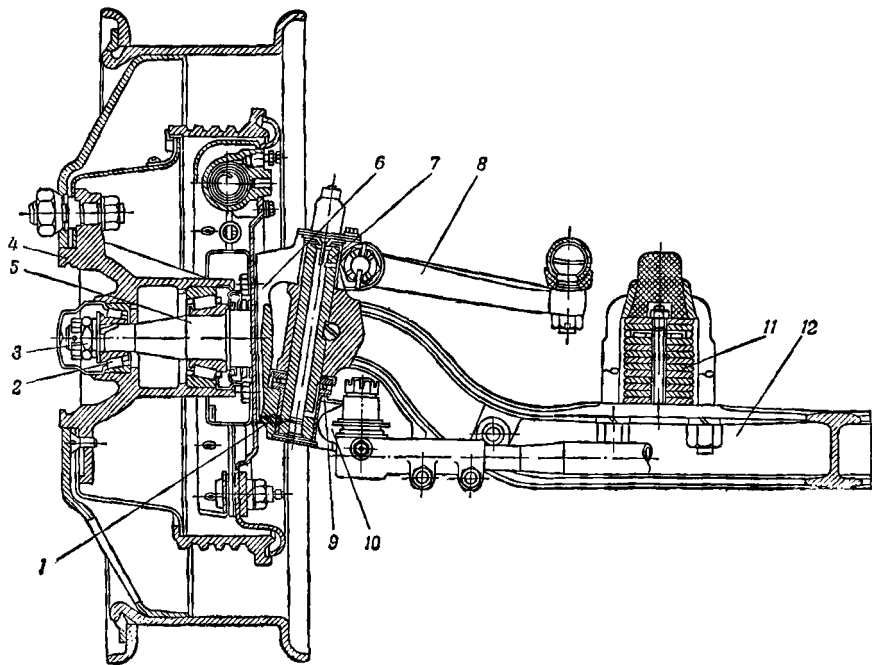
Передняя ось с поворотной цапфой и ступицей колеса в сборе (автомобиль ГАЗ-51).
